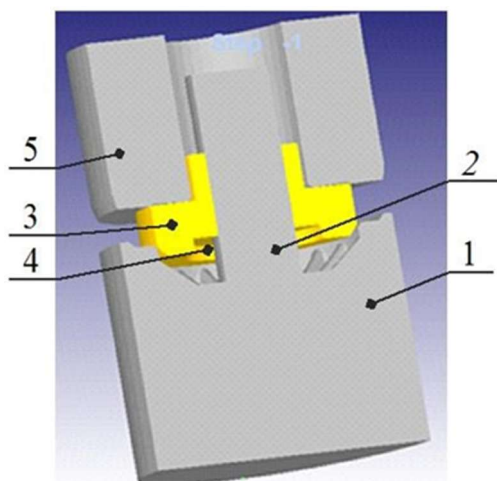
3D–модель инструмента и заготовки с кольцевой проточкой для штамповки конического зубчатого колеса:
